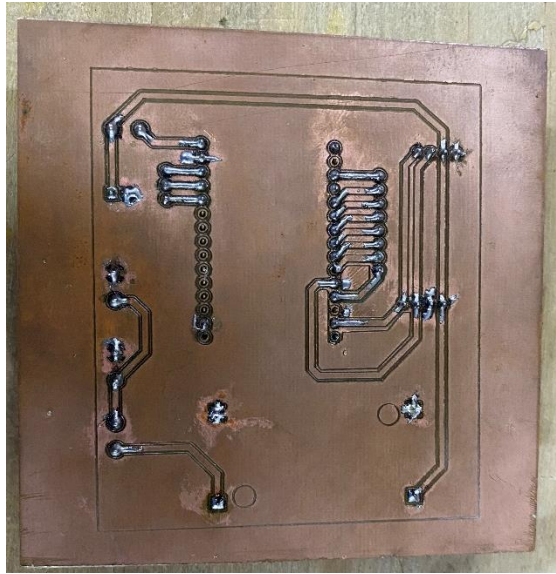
PCB con porta elementos electrónicos soldados. (Autores)
